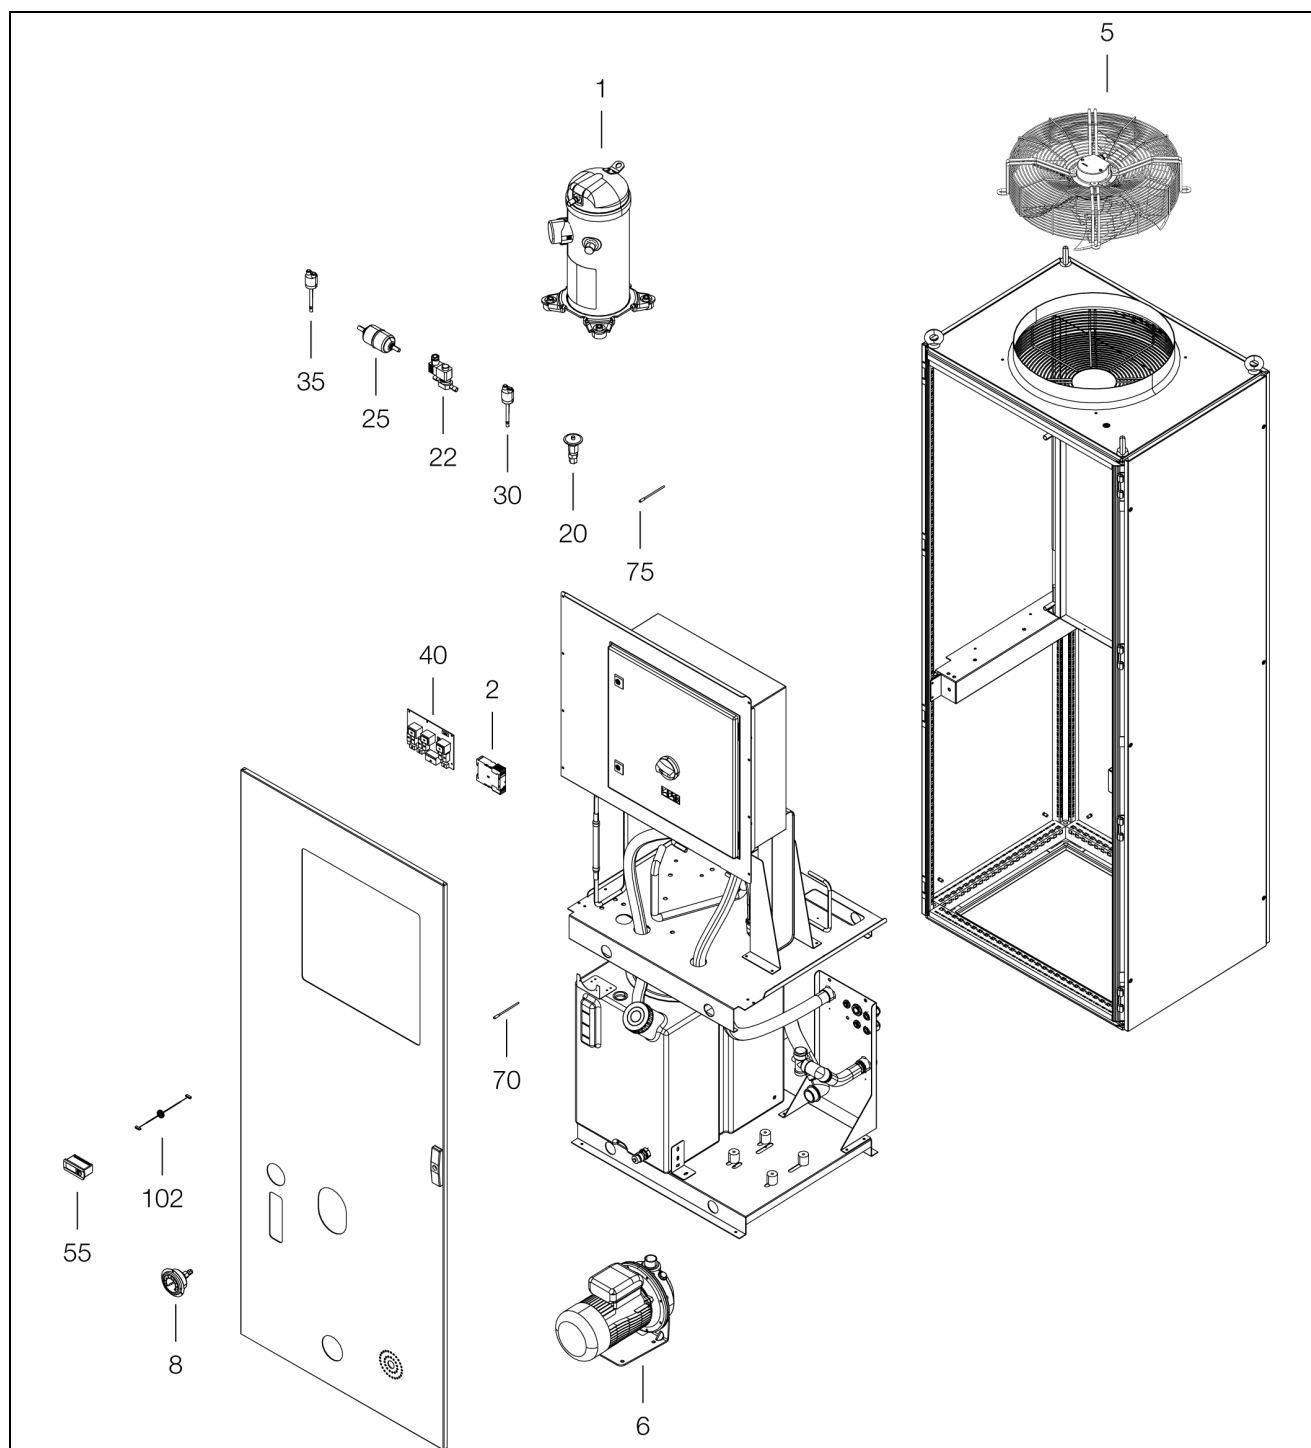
Pièces de rechange pour modèles 3335.790, 3335.830, 3335.840, 3335.850
